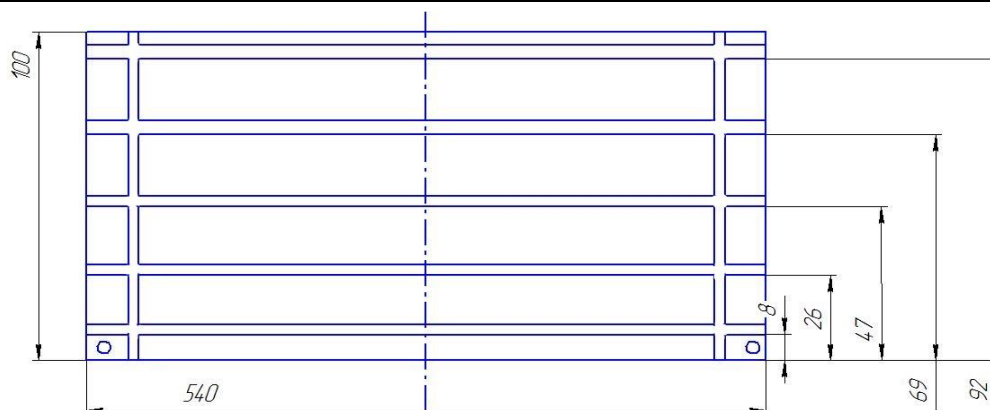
Фрагмент пластины с канавками для монтажа нагревателя
